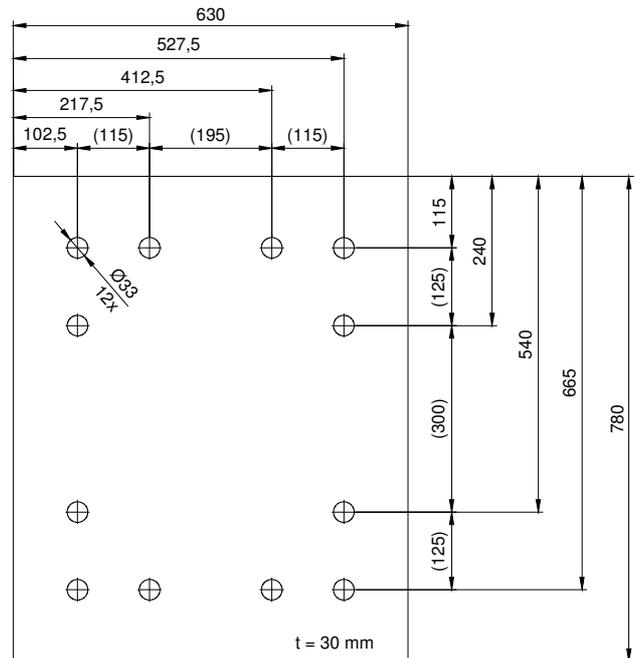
Lochbild auf der Anschraubfläche des Hydraulik-Magneten
